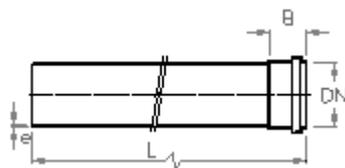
Tubo de PVC ponta lisa e bolsa
